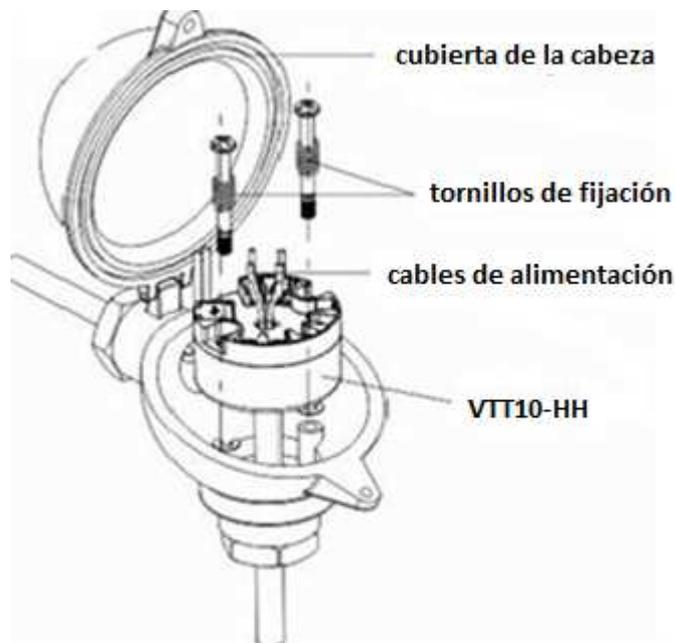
Esquema de montaje del VTT10-HH em cabeza.
